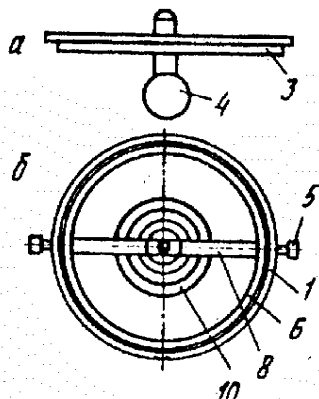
Вид сверху механизма без крышки (б) и вид крышки сбоку (а)
